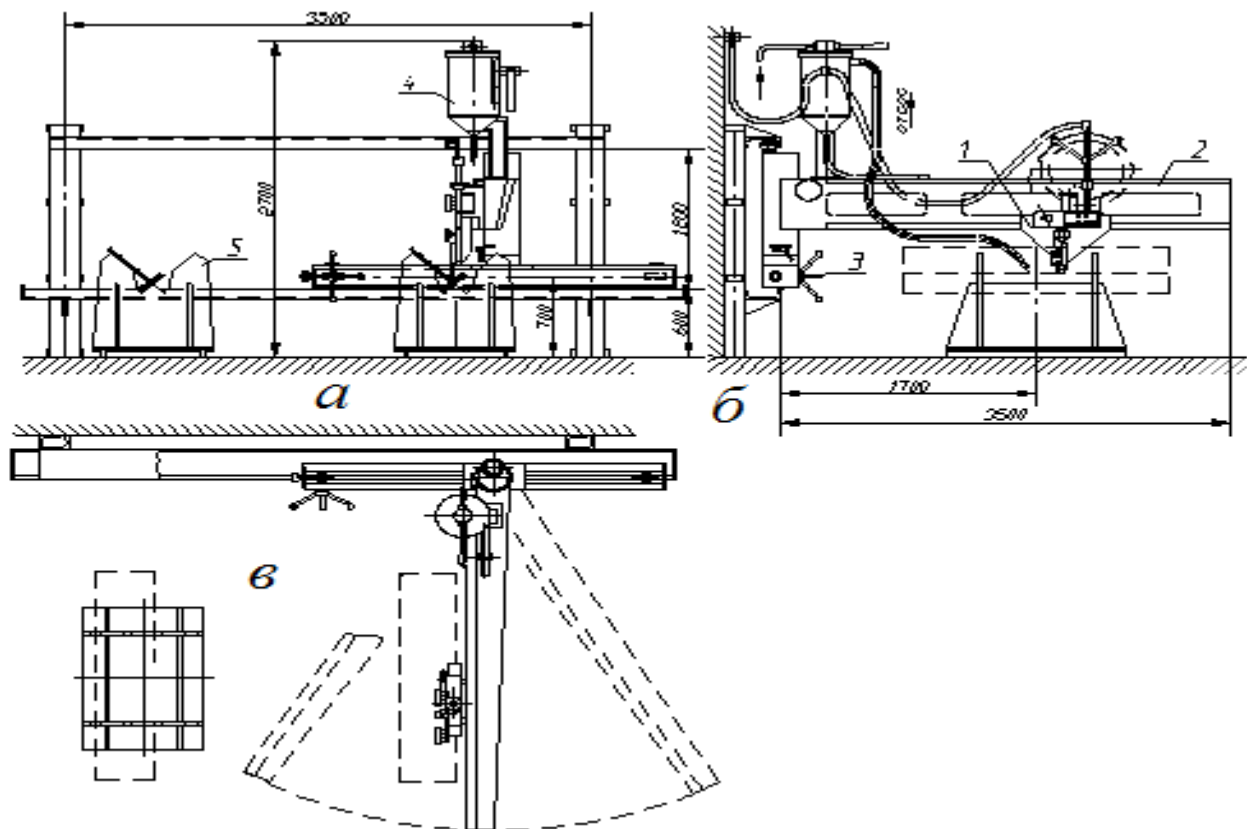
Установка із пересувною напрямною для зварювального апарата: а – вид з переду; б – вид з боку; в – вид зверху; 1 – самохідний зварювальний апарат; 2 – консольна напрямна; 3 – маховик для переміщення напрямної; 4 – флюсовий апарат; 5 – пристосування для розташування виробу (стіл або кантувач)
